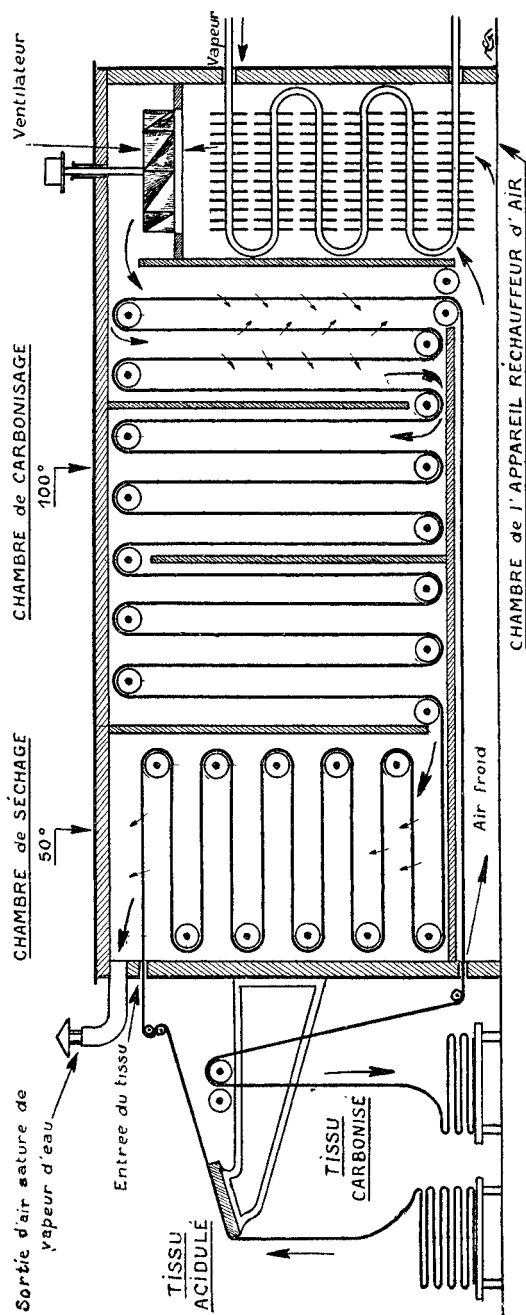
CARBONISAGE DES TISSUS DE LAINE. — *Machine carbonisense.
